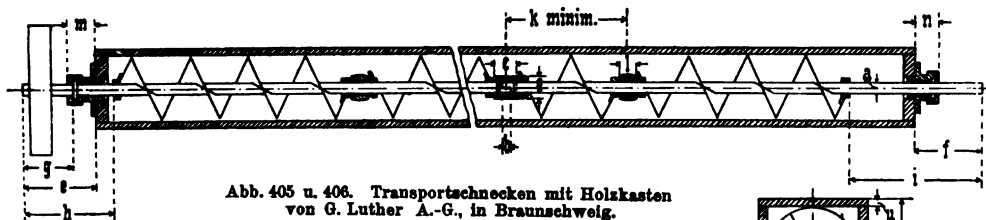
u. 406. Transportschnecken mit Holzkasten
